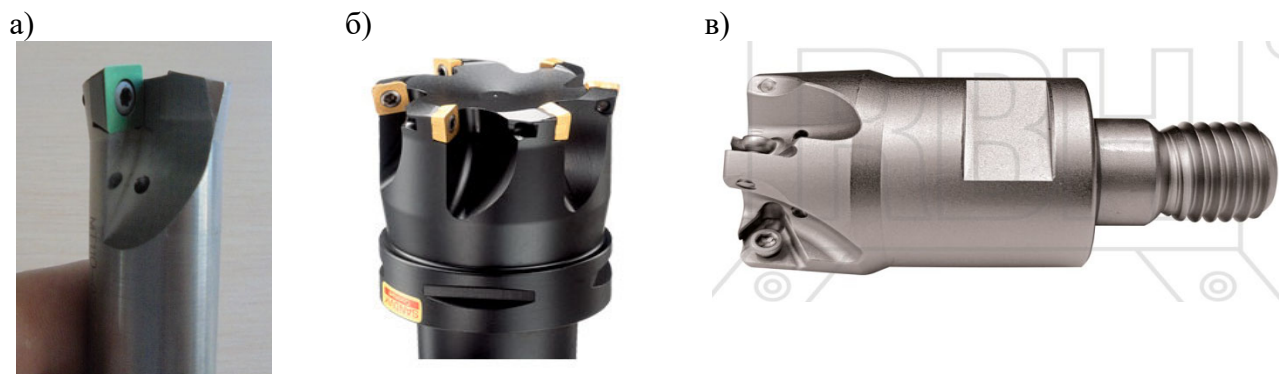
Режущая часть отечественной фрезы модели MT110-025225R02S009-ИК-T фирмы СКИФ-М (а); фреза (сменная головка) CoroMill R210 шведской фирмы Sandvik Coromant (б) и фреза Wincstar ICATPM 102020100 японской фирмы Mitsubishi (в)
